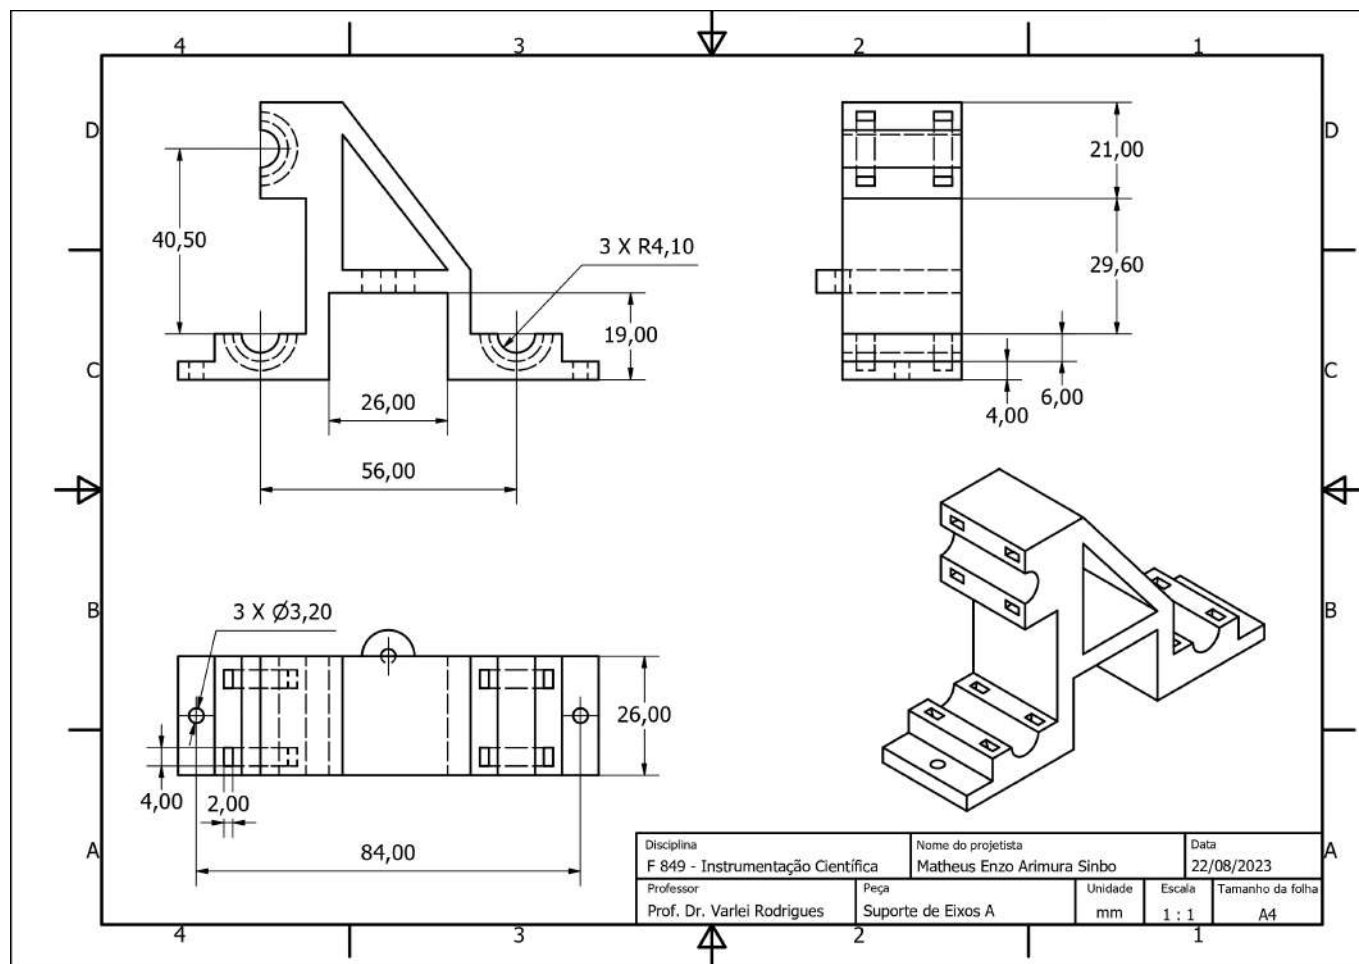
Desenho técnico do suporte dos eixos da carruagem para o lado A.
